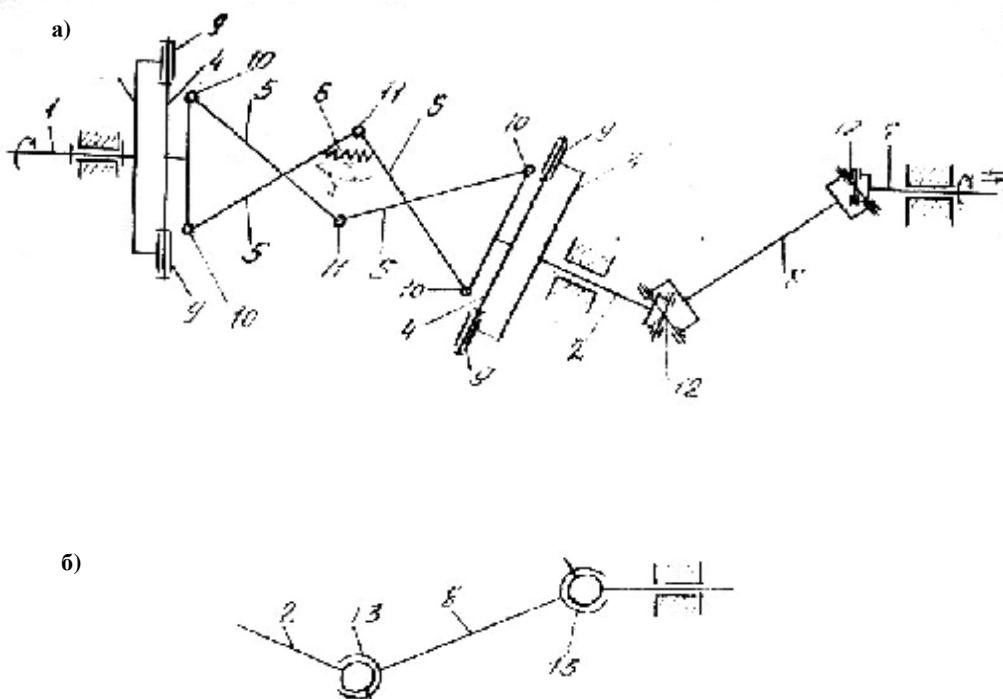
Кинематическая схема шарнирной муфты для соединения рычага с валом (а) и дополнительный вариант шарнирной муфты для соединения рычага с валом (б)
